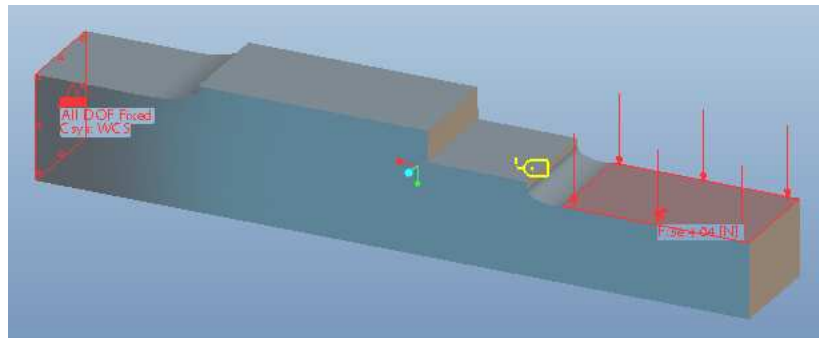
Cargas y restricciones del problema “Viga empotrada 2”
